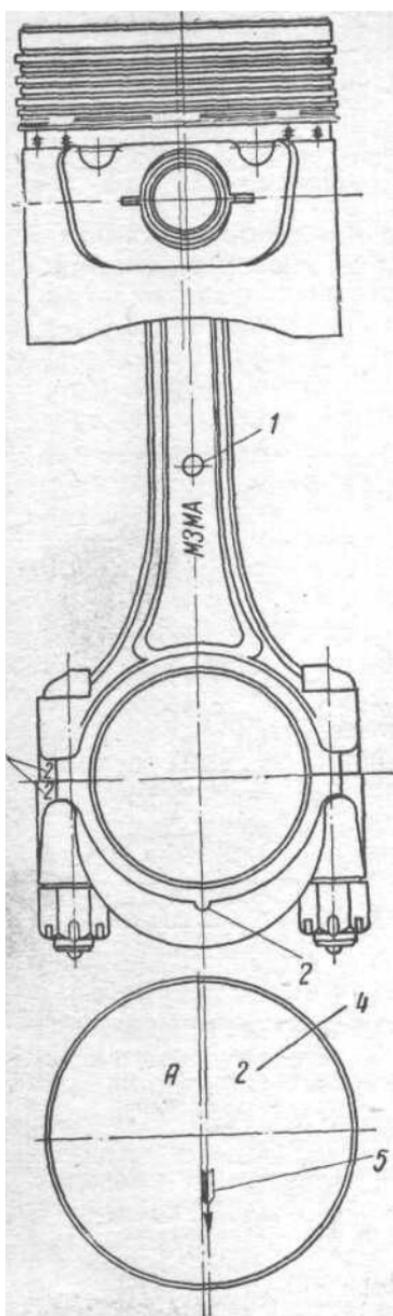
Установочные выступы и метки на поршне, шатуне и крышке шатуна:
